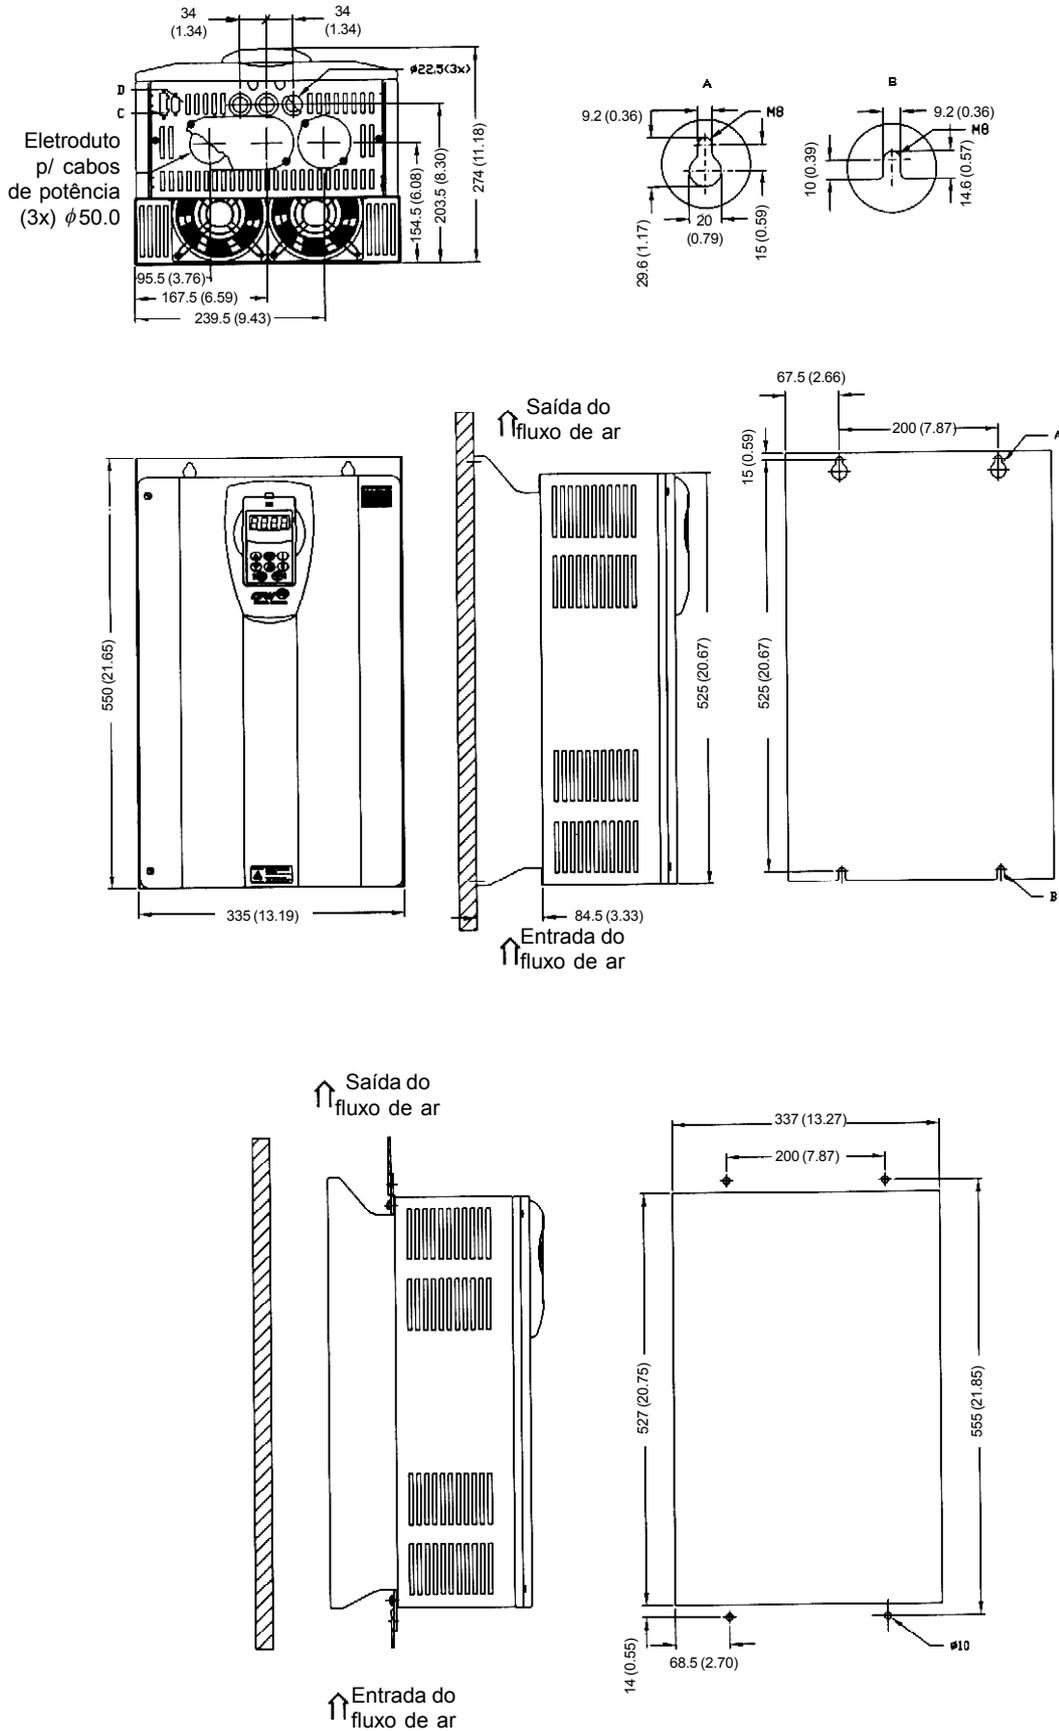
Mecânica 5 - Dimensões em mm (polegadas)
